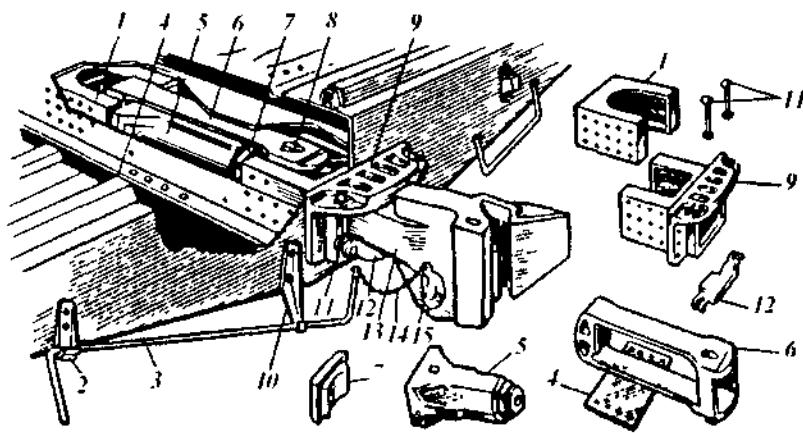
Автосцепное устройство вагона: 1 — упоры задние; 2 — кронштейн; 3 — двуплечий рычаг; 4 — поддерживающая планка; 5 — поглощающий аппарат; 6 — тяговый хомут; 7 — упорная плита; 8 — клин; 9 — ударная розетка; 10 — державка; 11 — маятниковые подвески; 12 — центрирующая балочка; 13 — корпус автосцепки; 14 — цепь; 15 — валик подъемника
